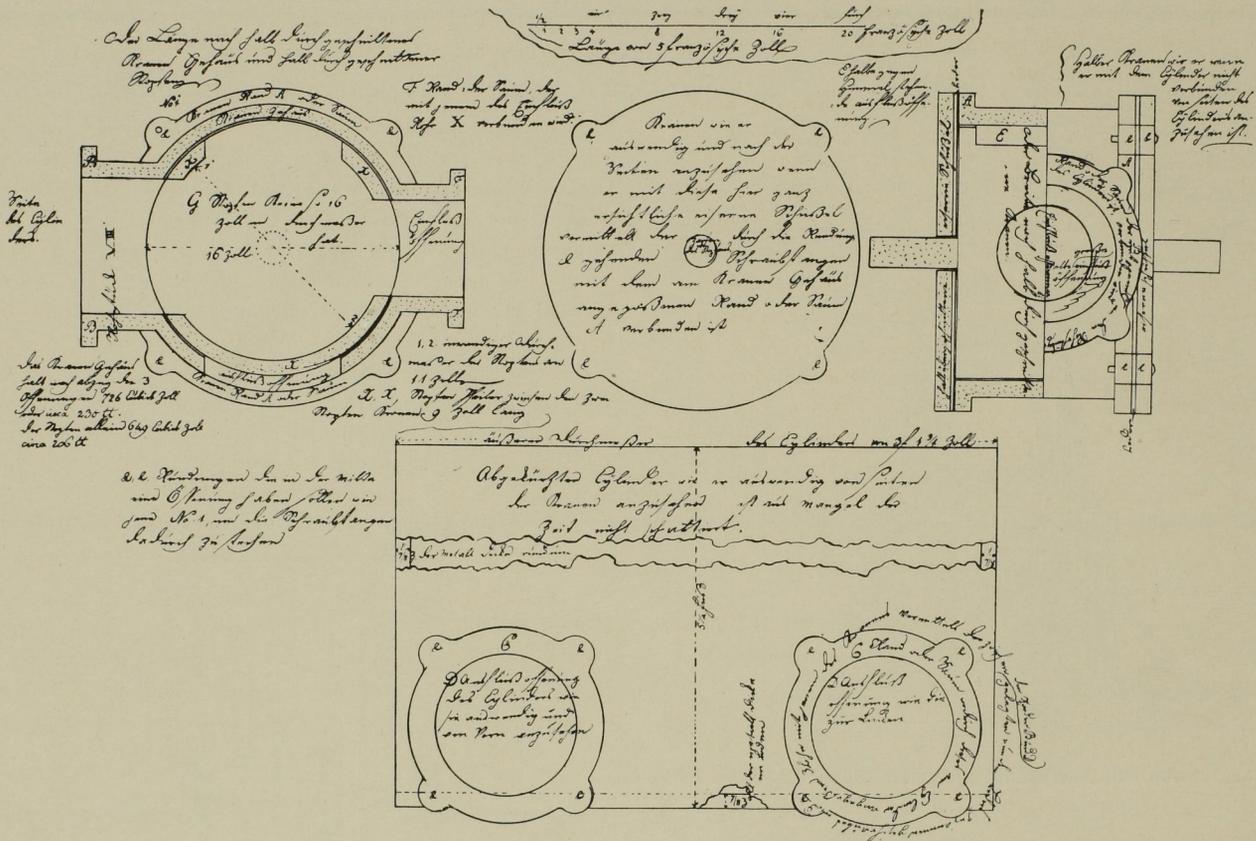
Werkzeichnung des Cylinders einer Wassersäulen-Maschine.
